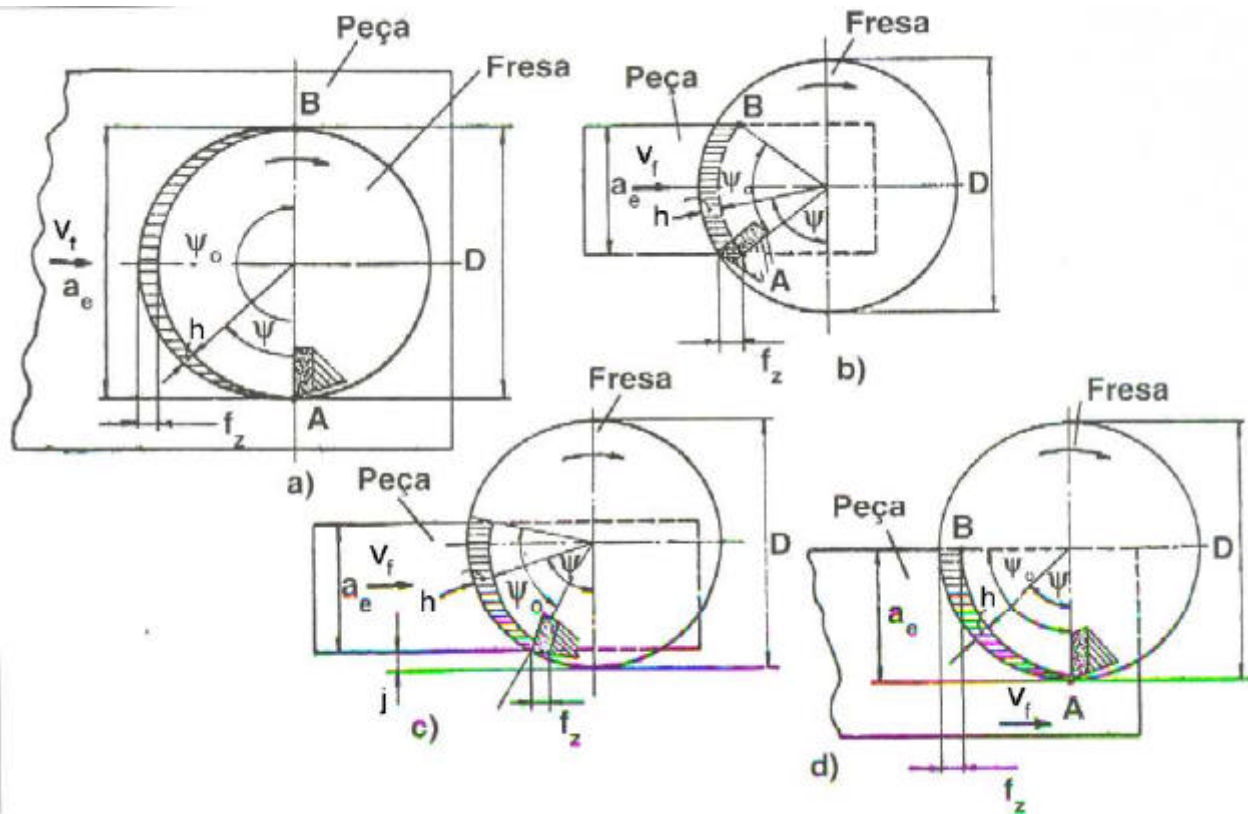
Fresamento Frontal : a) simétrico de rasgo, b) simétrico comum, c) assimétrico com usinagem total da superfície d) assimétrico com usinagem parcial
